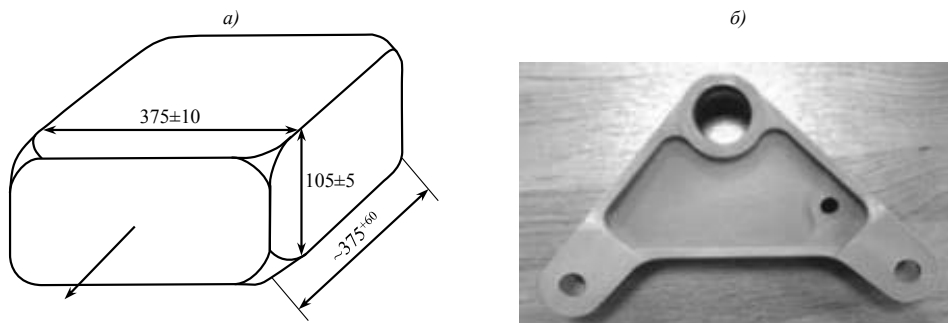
Схематический чертеж поковки (а) из сплава ВМД16 и внешний вид детали «кронштейн-качалка» (б)
